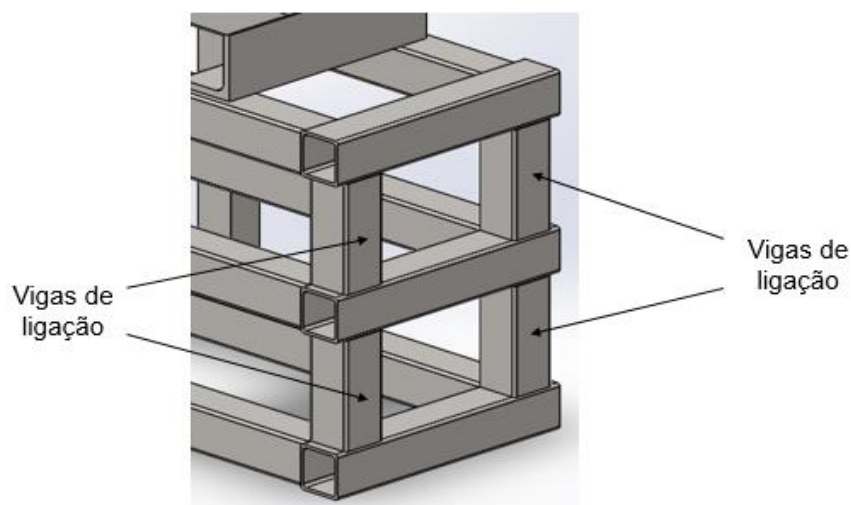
Vista da extremidade anterior da posição de serviço das vigas de ligação
